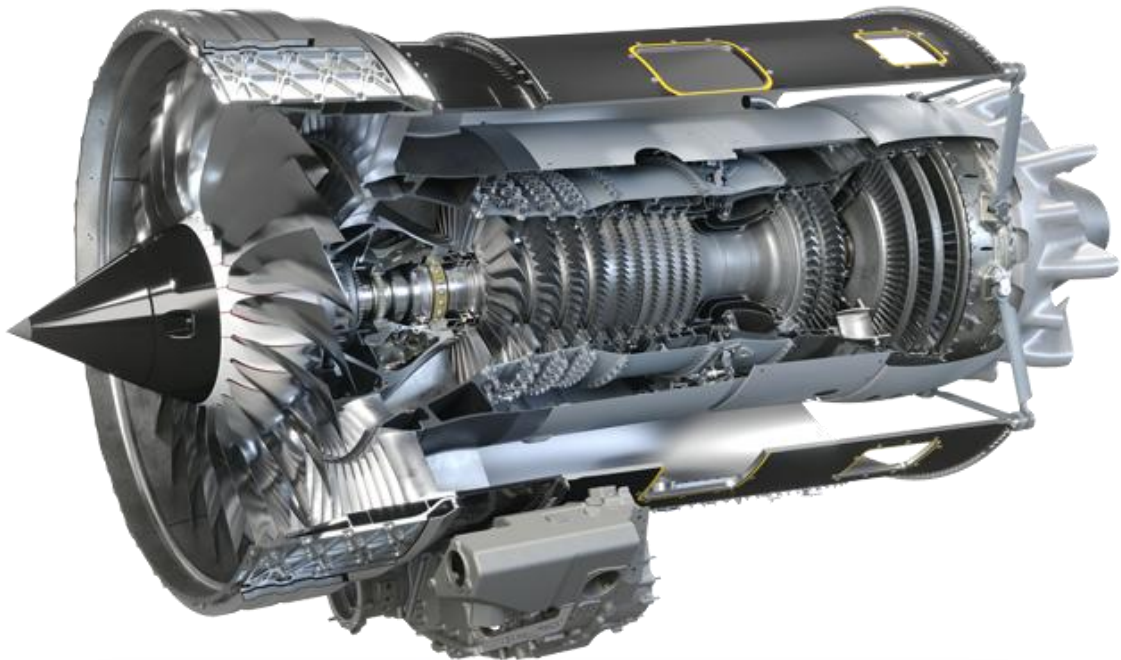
Princíp konštrukcie leteckého motora [1].
